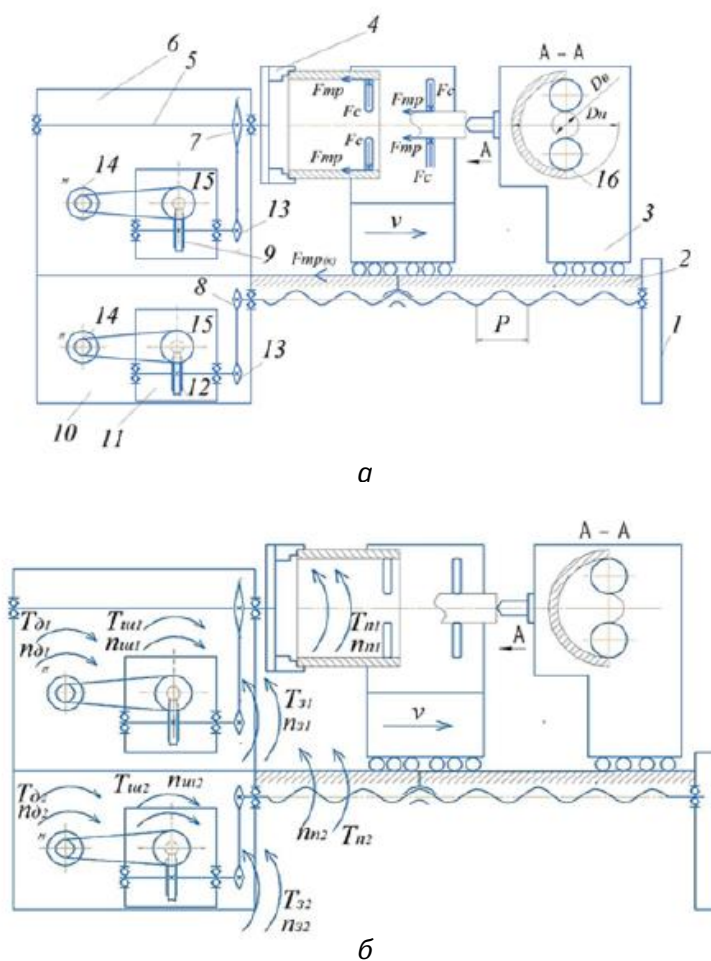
Схема установки «011-1-10» «Ремдеталь»: а — компоновочная для определения сил: 1 — задняя тумба; 2 — направляющие; 3 — задняя бабка; 4 — трехкулачковый самоцентрирующий патрон; 5 — шпиндель; 6 — передняя бабка; 7 — звездочка $Z=40$; 8, 13 — звездочки $Z=20$; 9, 12 — червячные колеса; 10 — тумба передняя; 11 — червячные редукторы 2Ч-63 (1:50); 14 — шкивы двигателя $D=70,35$; 15 — шкивы редуктора $D=165$; 16 — электрод-ролик; 17 — двигатели ПС-41 (0,25 кВт); $Dв$ — диаметр обрабатываемых наружных поверхностей (20–200 мм); $Dн$ — диаметр обрабатываемых внутренних поверхностей (60–250 мм); P — шаг винта (10 мм); б — для определения скоростей и моментов кинематических звеньев
